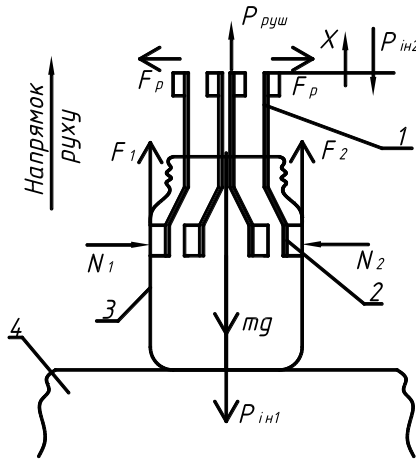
Схема дії сил під час піднімання шару банок із транспортного пакета: 1 – пружний елемент; 2 – гумова накладка; 3 – банка; 4 - транспортний пакет
